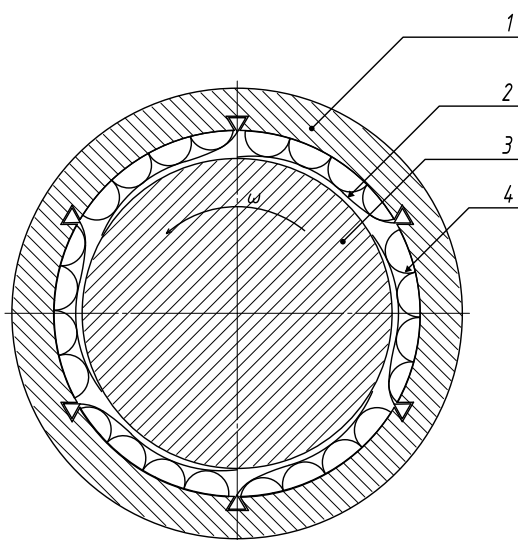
Схема конструкции лепесткового подшипника на газовой смазке. 1 – статор; 2 – лепестки; 3 – вал; 4 – гофрированный элемент.
